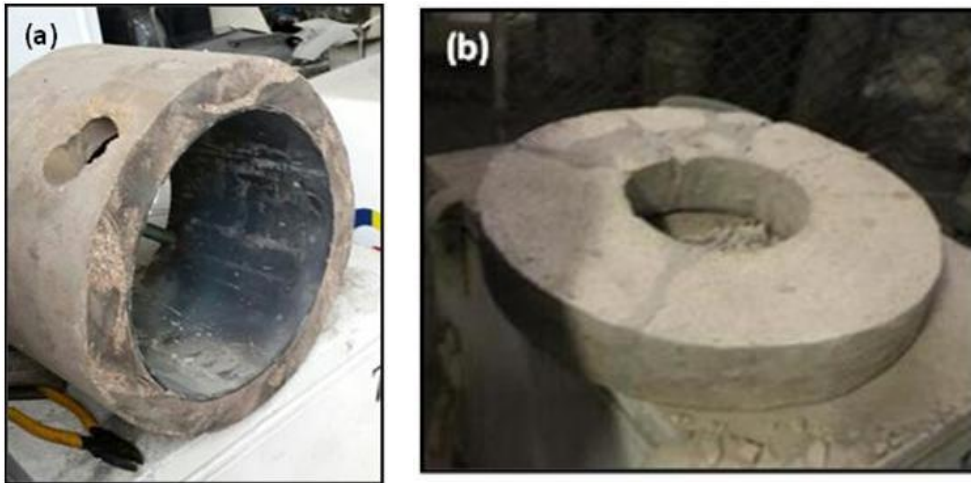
Piezas desmoldadas listas para ser resanadas: (a) paredes del horno. (b) base de horno.
